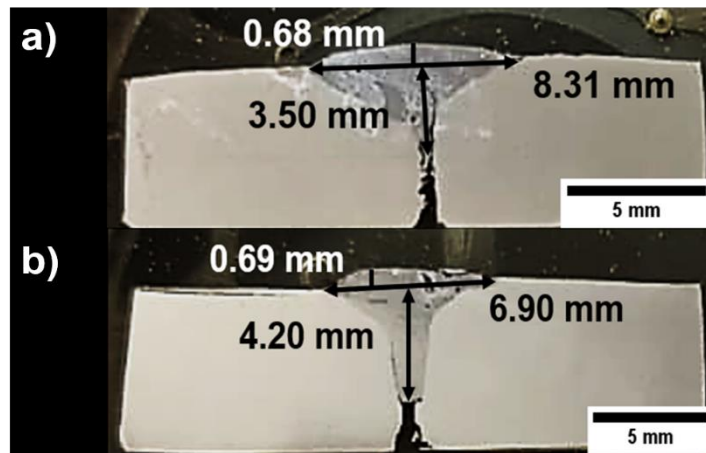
86 Unión de las placas de aleación de aluminio a) Soldadura 14 y b) réplica de la soldadura 14.
